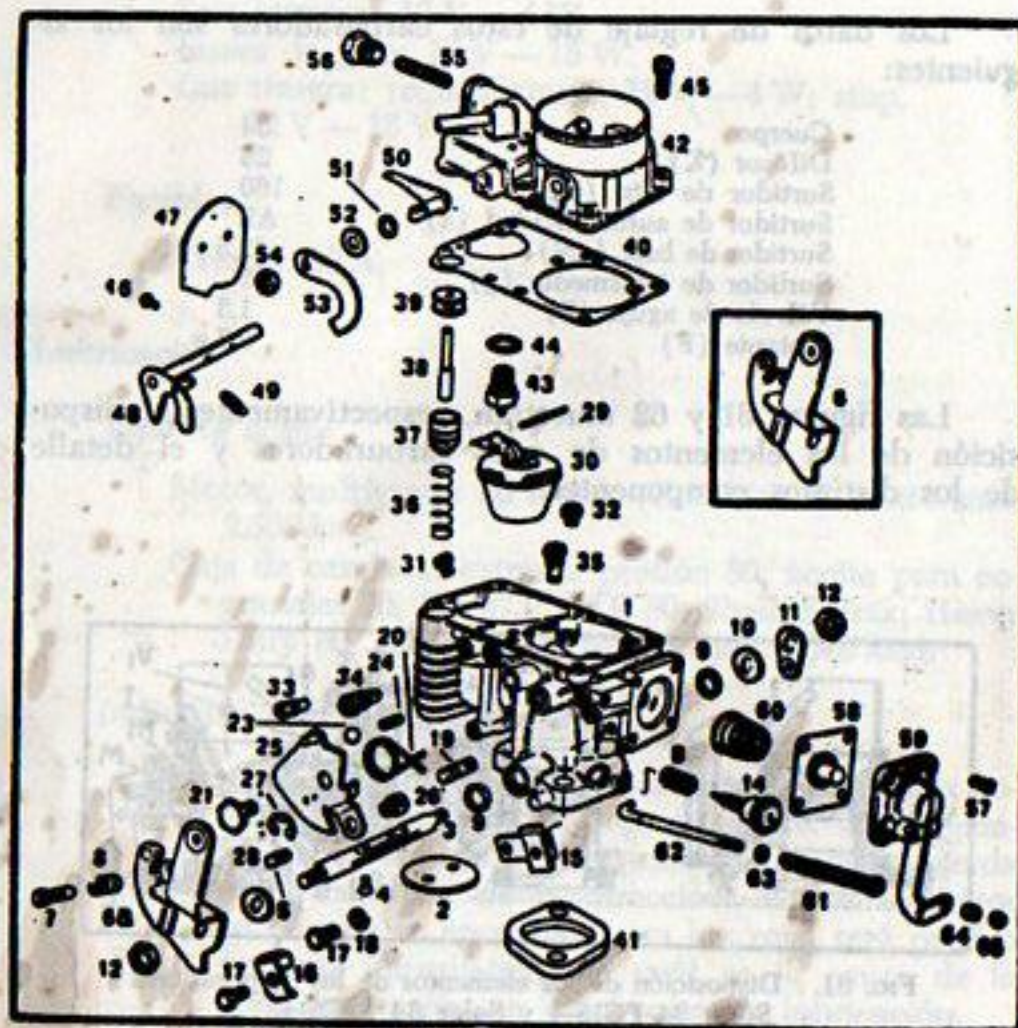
Componentes de los carburadores Solex 34 PCIS-4 y Solex 34 PICS-4.
